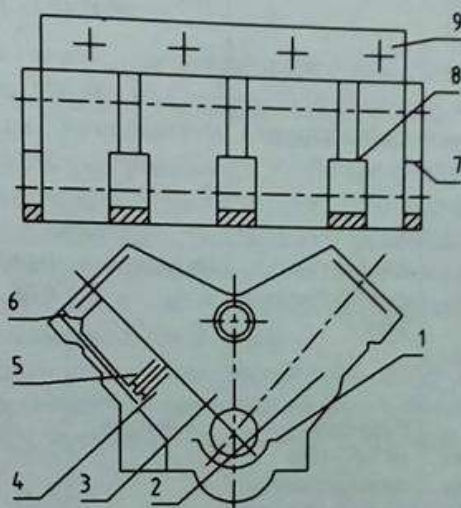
Твердість блока циліндрів — HB 187-241; кришок вальниць — HB 121-163
